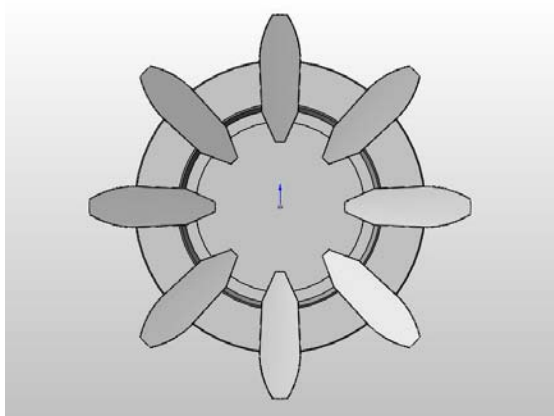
Conceção sistema fixar / trilhar espindel em aço inox - vista frontal.
